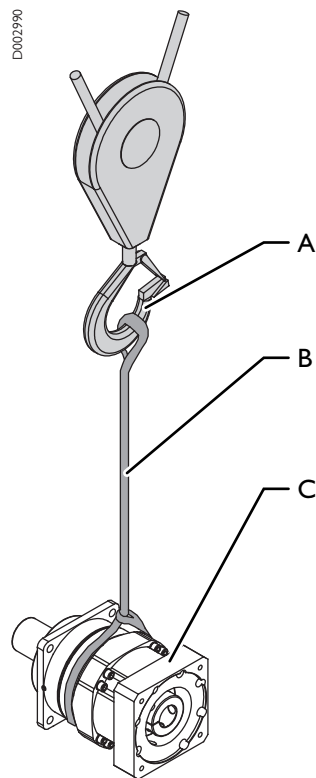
Fixer le dispositif de levage : Engrenage planétaire
